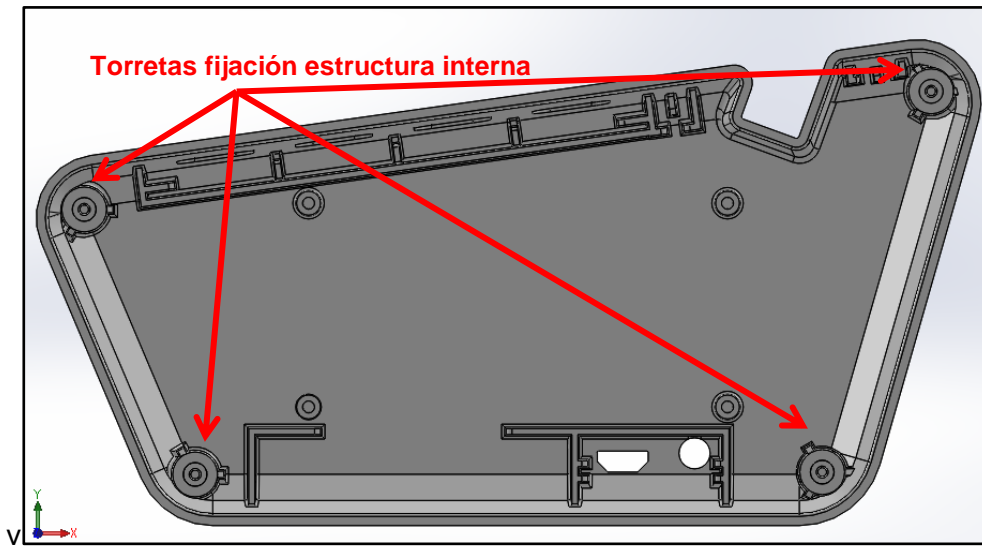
Vista de la posición de las torretas de fijación de la estructura interna.
